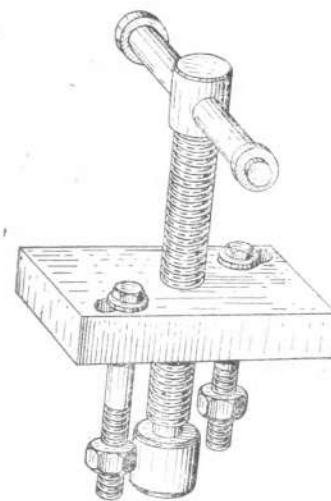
Приспособление для снятия маховика и корпуса заднего подшипника
